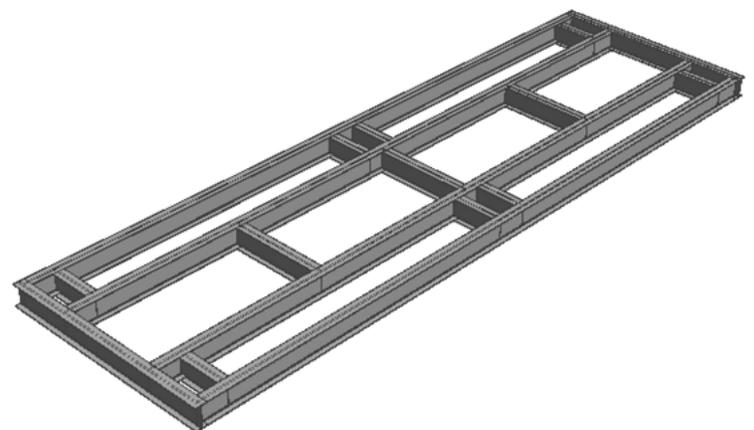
Estructura viga laminada soldada. Modelo de elaboración propia.
